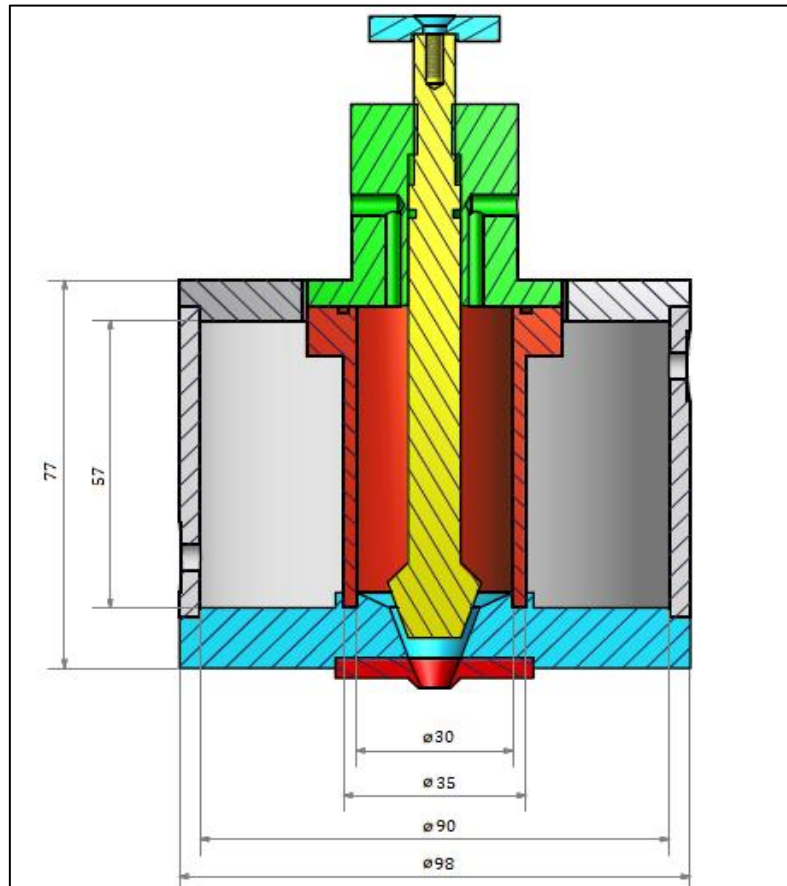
Dimensions (en mm) du générateur de gouttes
